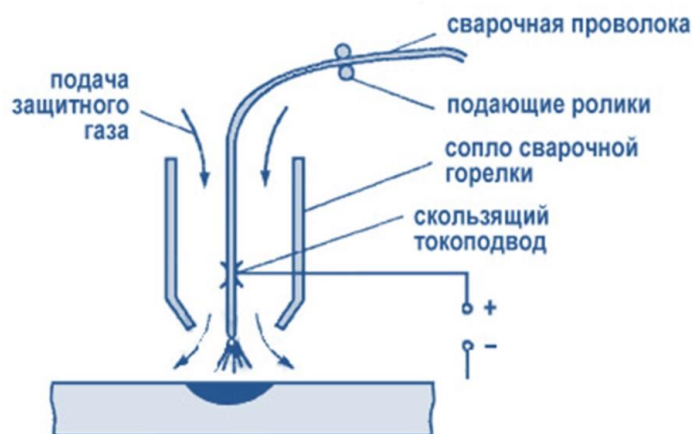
Механизированная сварка плавящимся электродом в инертном газе
